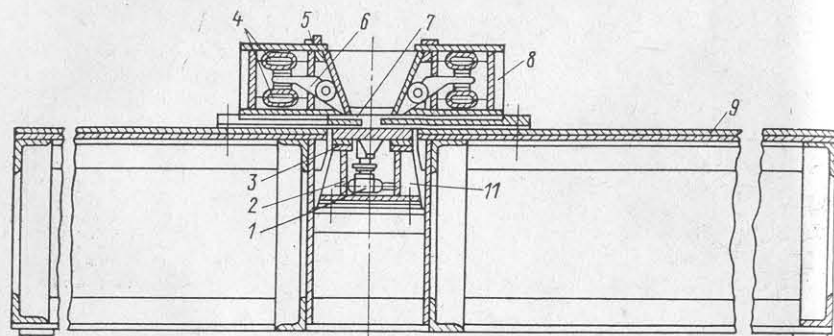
Стенд для сборки и автоматической сварки полотнищ рычажного типа.
